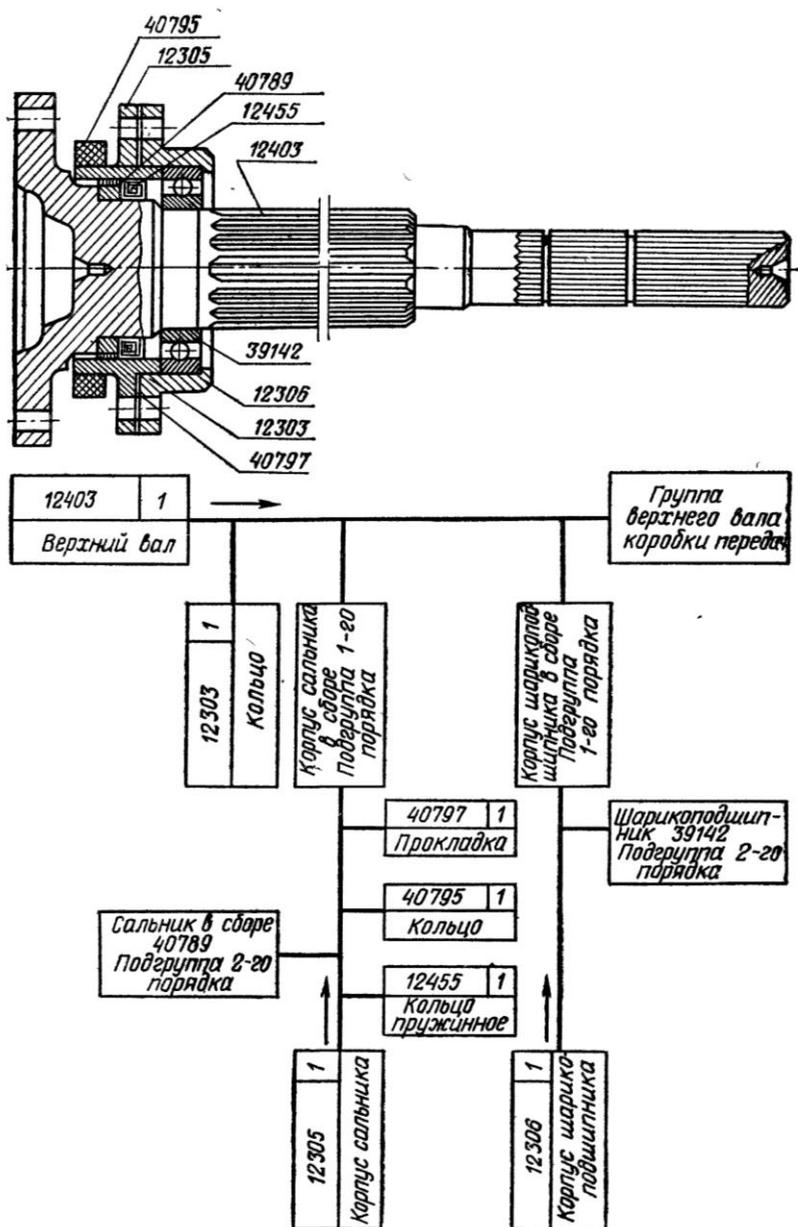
Чертеж верхнего вала коробки передач и технологическая схема его сборки
